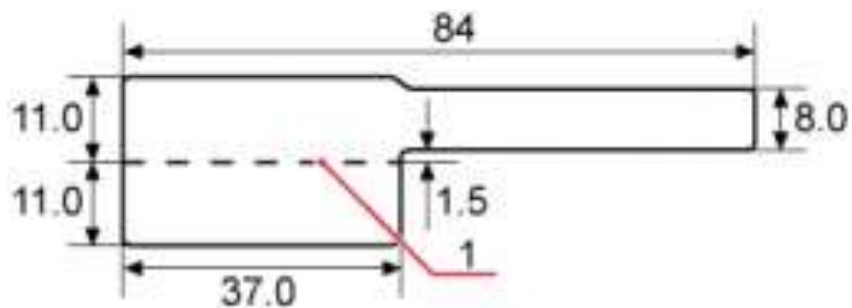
Dimensiones y diseño del etiquetado tipo L.
